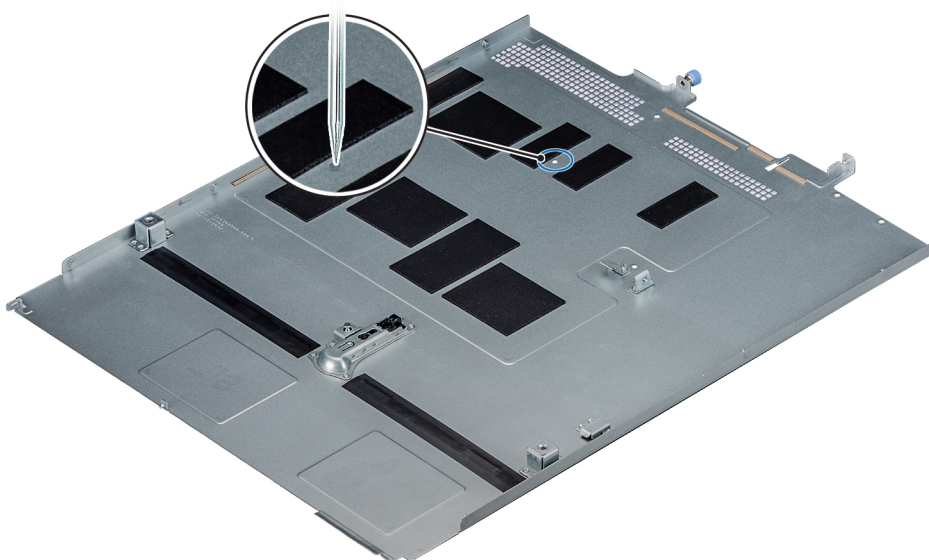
Freilegen der Schraubenbohrung für die Abstandhalter-Sechskantdistanzschraube
